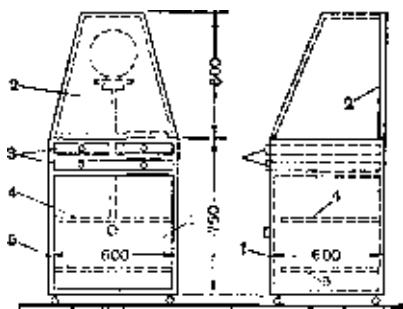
Эскизный чертеж тумбочки для фотоувеличителя: 1— основание тумбочки; 2— колпак-футляр для фотоувеличителя; 3— ящики для фотобумаги; 4—5—полочки для различного оборудования. Размеры в мм
